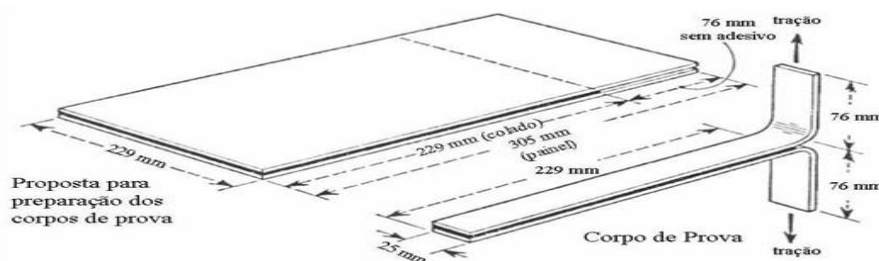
Dimensões para ensaio T-PEEL segundo ASTM 1876
